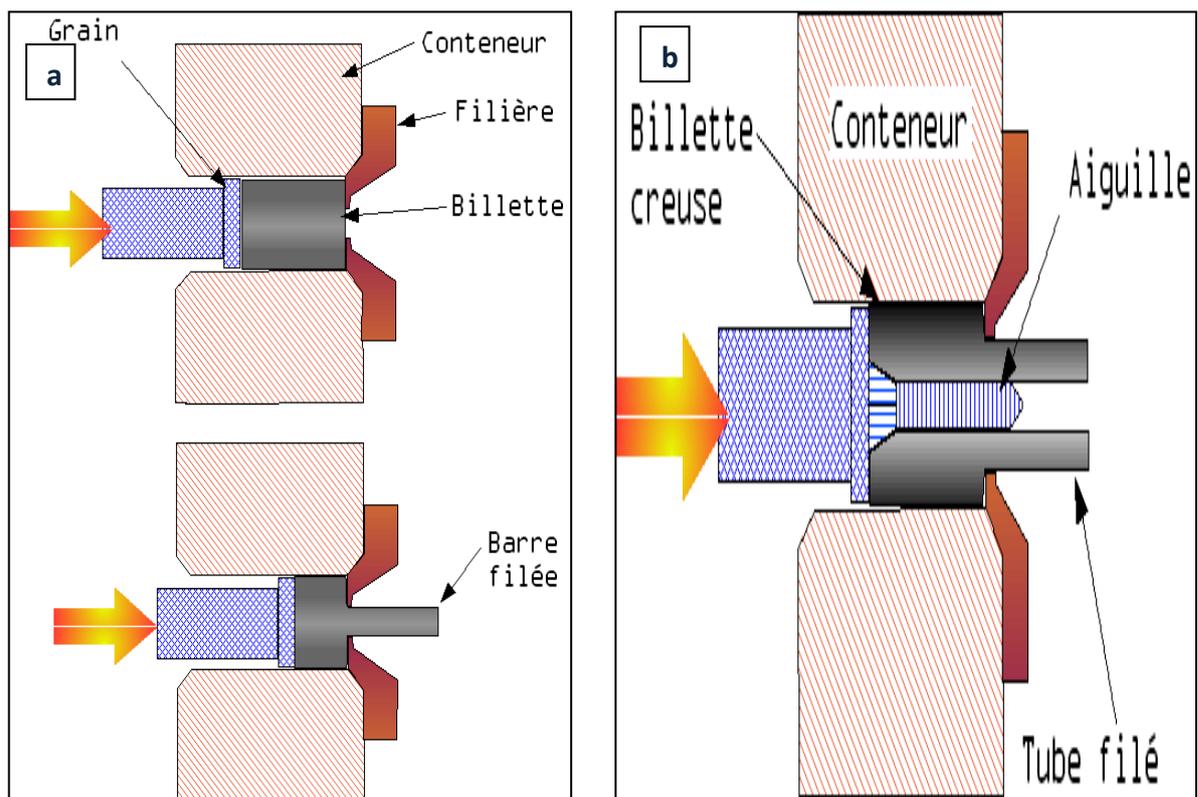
a) Extrusion de formes pleines, b) Extrusion de formes creuses par aiguilles [6]
